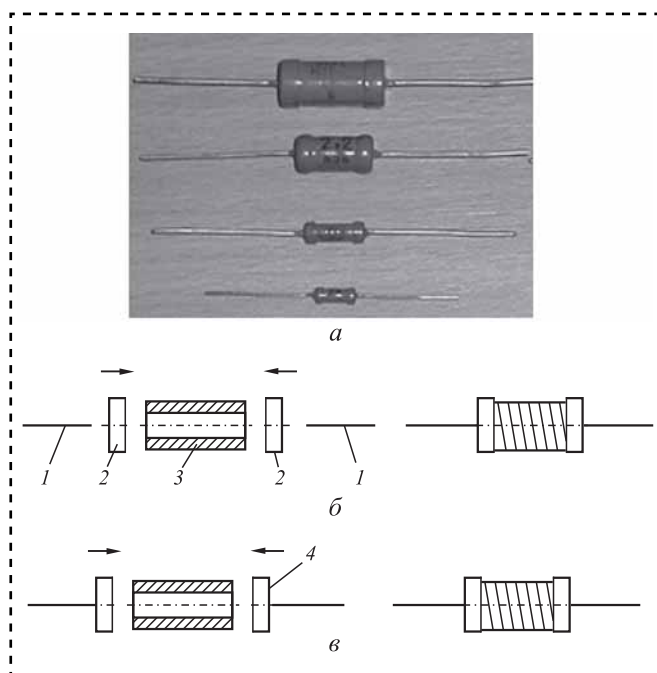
Внешний вид (а) и конструктивные схемы резистора типа МЛТ с приваркой (б) и без приварки (в) контактных выводов (колпачок изготовлен заодно с выводом):
